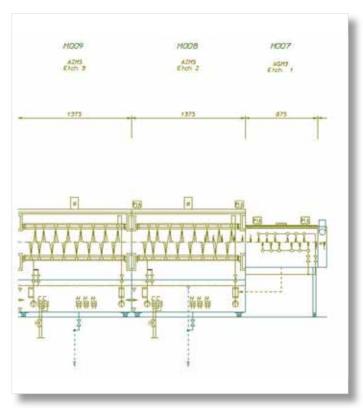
Detailansicht aus einem Modul für die Leiterplattenproduktion mit diversen Symbolen für Pumpen, Ventile uvm. (Angebotszeichnung)
